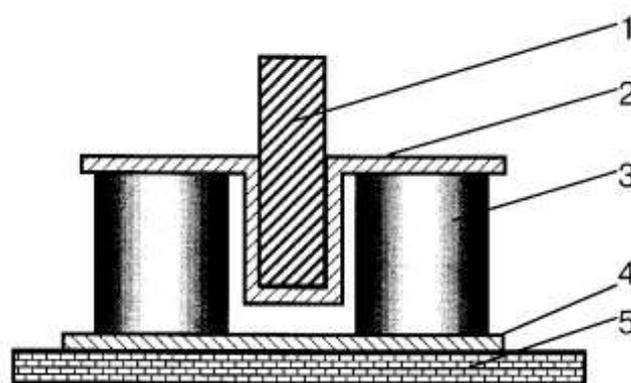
Конструктивная схема резинового виброизолятора обычного типа: 1–лапа станка; 2–S-образный кронштейн; 3–резиновый упругий элемент; 4–опорная поверхность; 5–межэтажное перекрытие.
